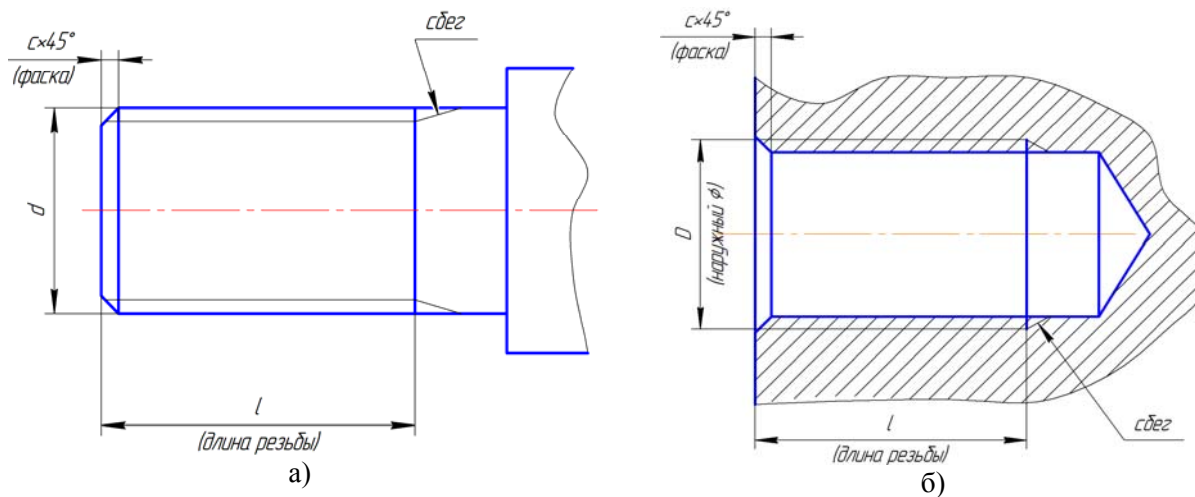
Изображение сбega резьбы на чертеже: а – на стержне; б – в отверстии
